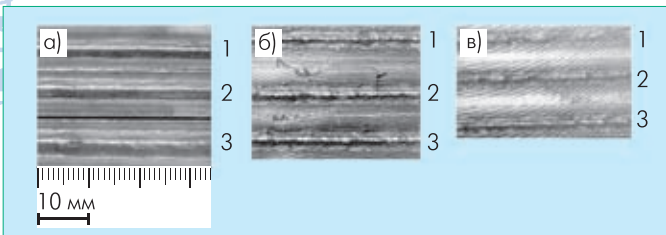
Лицевая поверхность сварных швов на низколегированной стали, выполненных в гелии (а), в азоте (б), в двуокиси углерода (в) при мощности излучения 8 кВт и скорости сварки 20 (1), 16 (2), 12 (3) мм/с. Сварка выполнялась авторами [11, 19]
